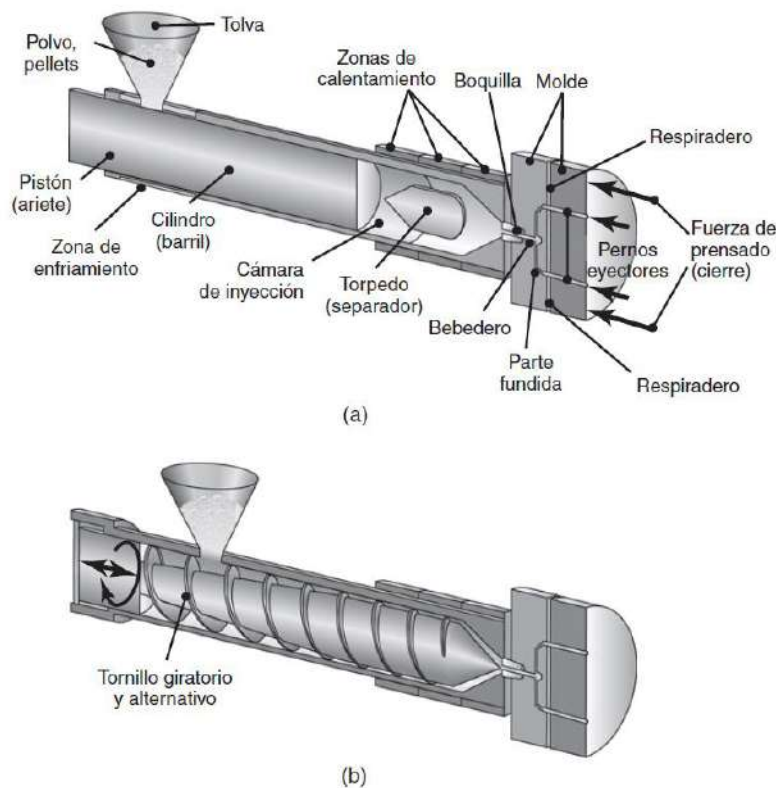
máquina de moldeo por inyección, del tipo de tornillo recíprocante [1]
